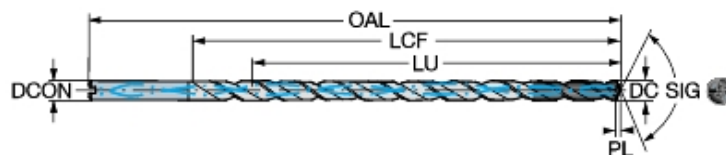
Geometría de la broca CoroDrill 861 861.1-0900-180A1-GMGC34
